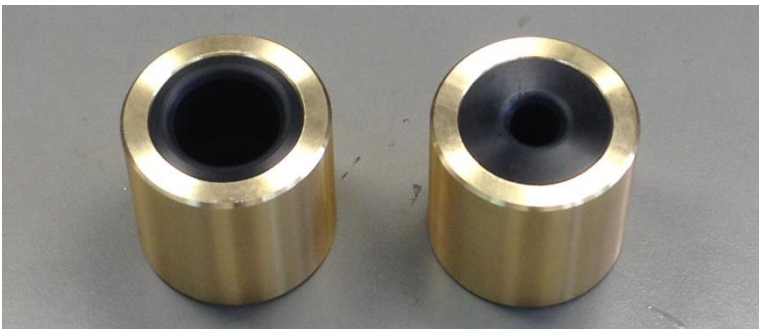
Aufsätze (für 25mm- und 12mm-Sensoren)
